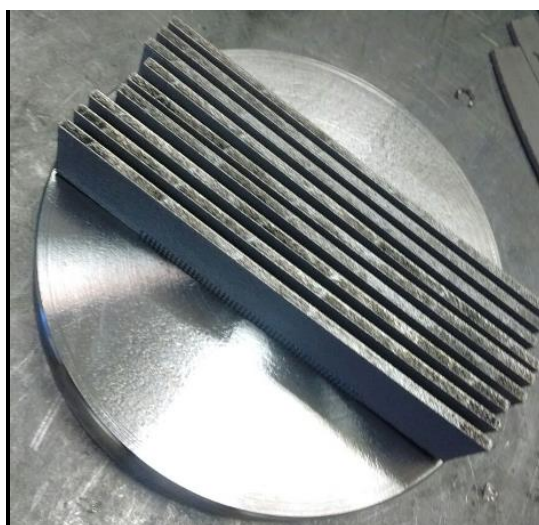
Внешний вид образцов изготовленного СЛС
